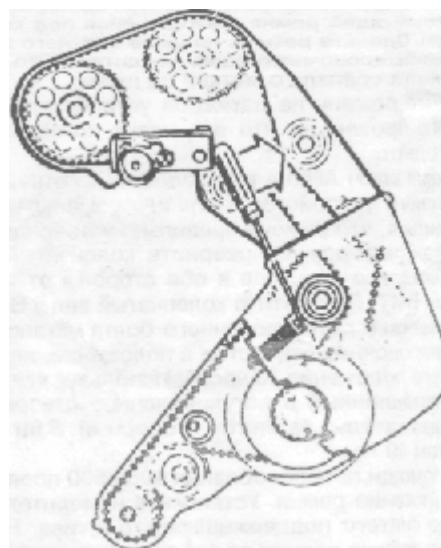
Регулировка приводного ремня Двигатель В234F
